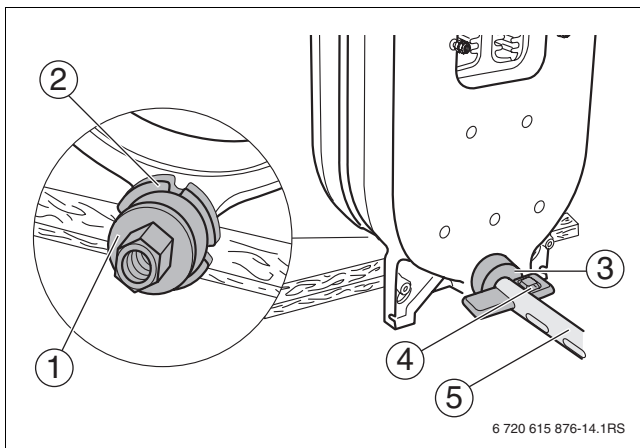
Outil de serrage monté sur le moyeu inférieur
